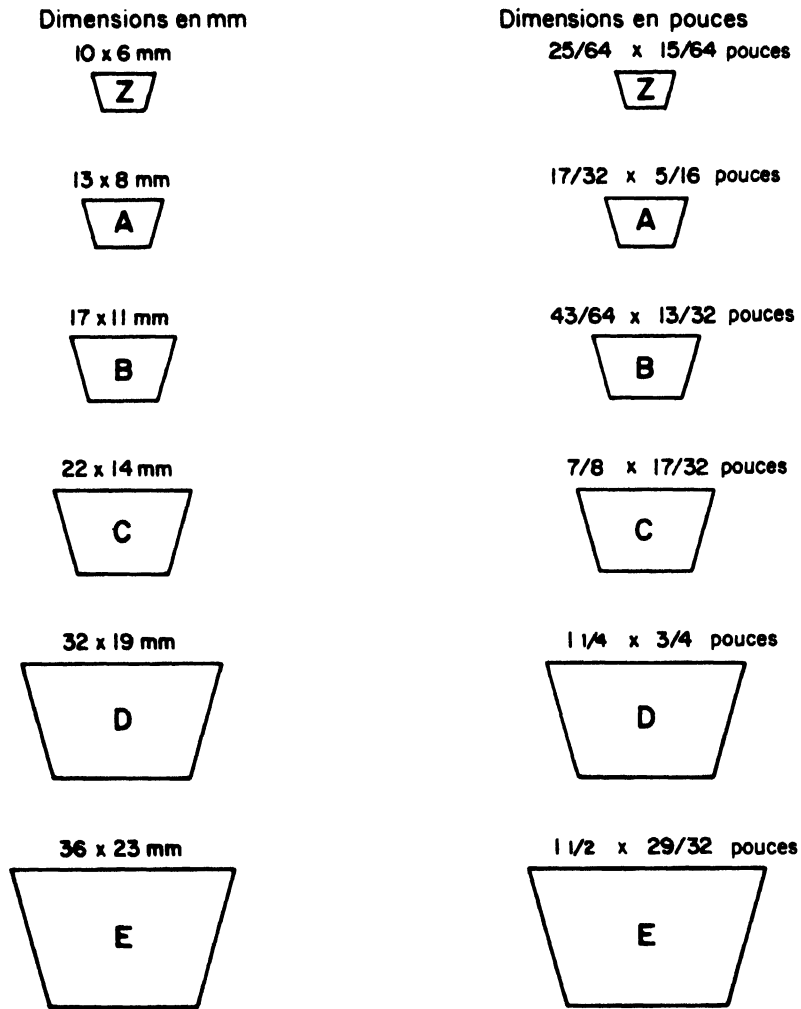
COUPE DE COURROIES TRAPEZOIDALES
